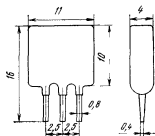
Габаритные и присоединительные размеры фильтров ФП1П8-62 и ФП1П8-63
